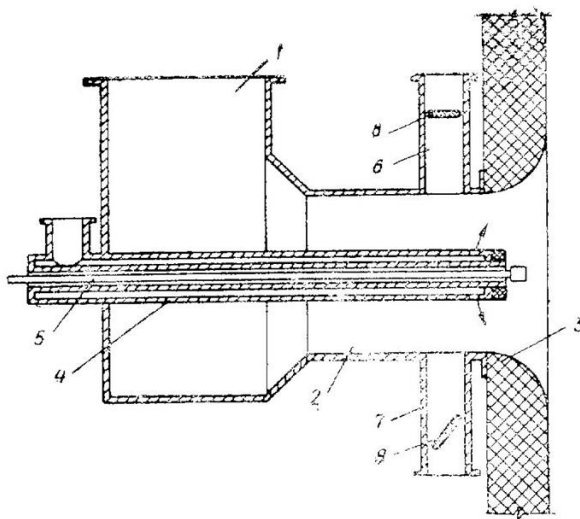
Прямоточная поворотная горелка (1 – короб для подачи воздуха; 2 – канал подачи воздуха; 3 – тороидальный диффузор; 4 – труба для подачи топлива; 5 – мазутная форсунка; 6,7 – трубы для подвода дополнительного воздуха; 8,9 – регулирующие шиберы)
